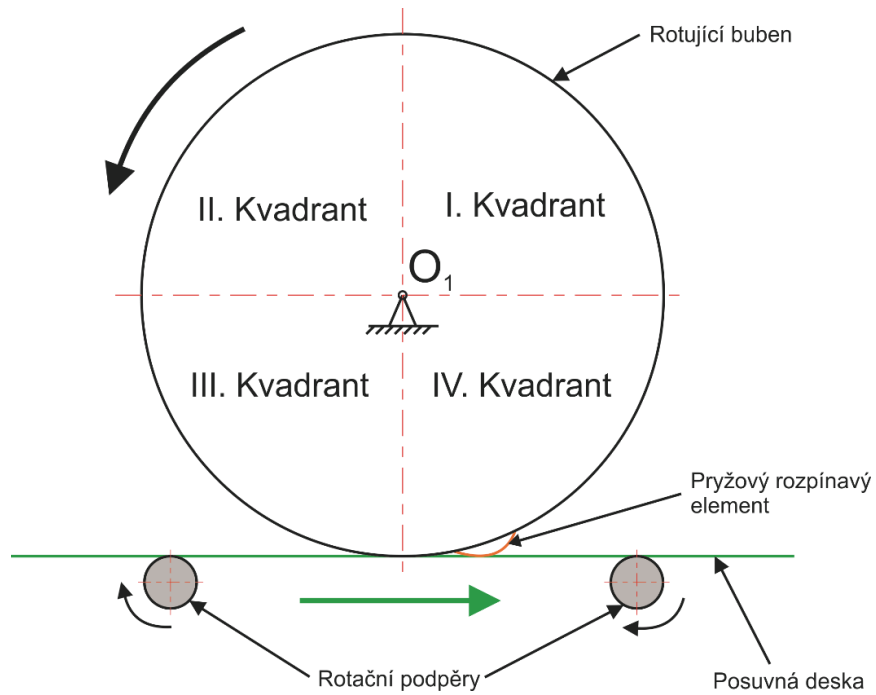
Princip přetlakového pomaluběžného pneumotoru 1
